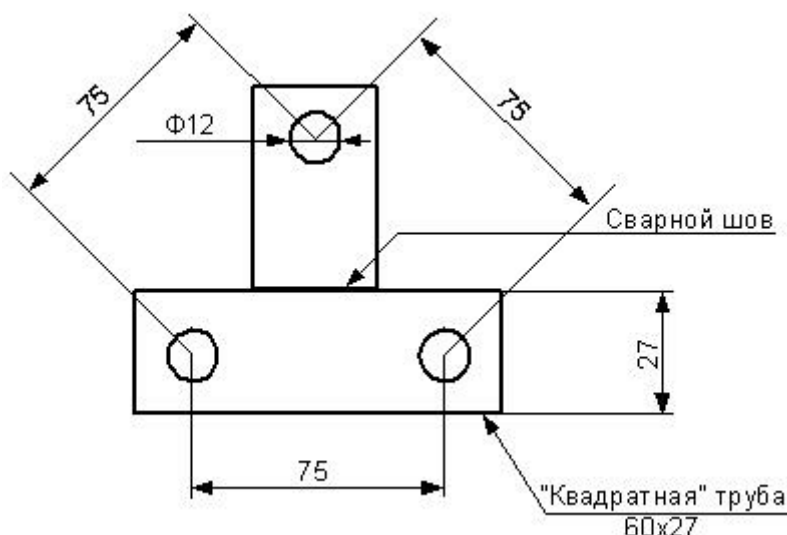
Проставка под платформу рычагов КПП (вид сверху).
